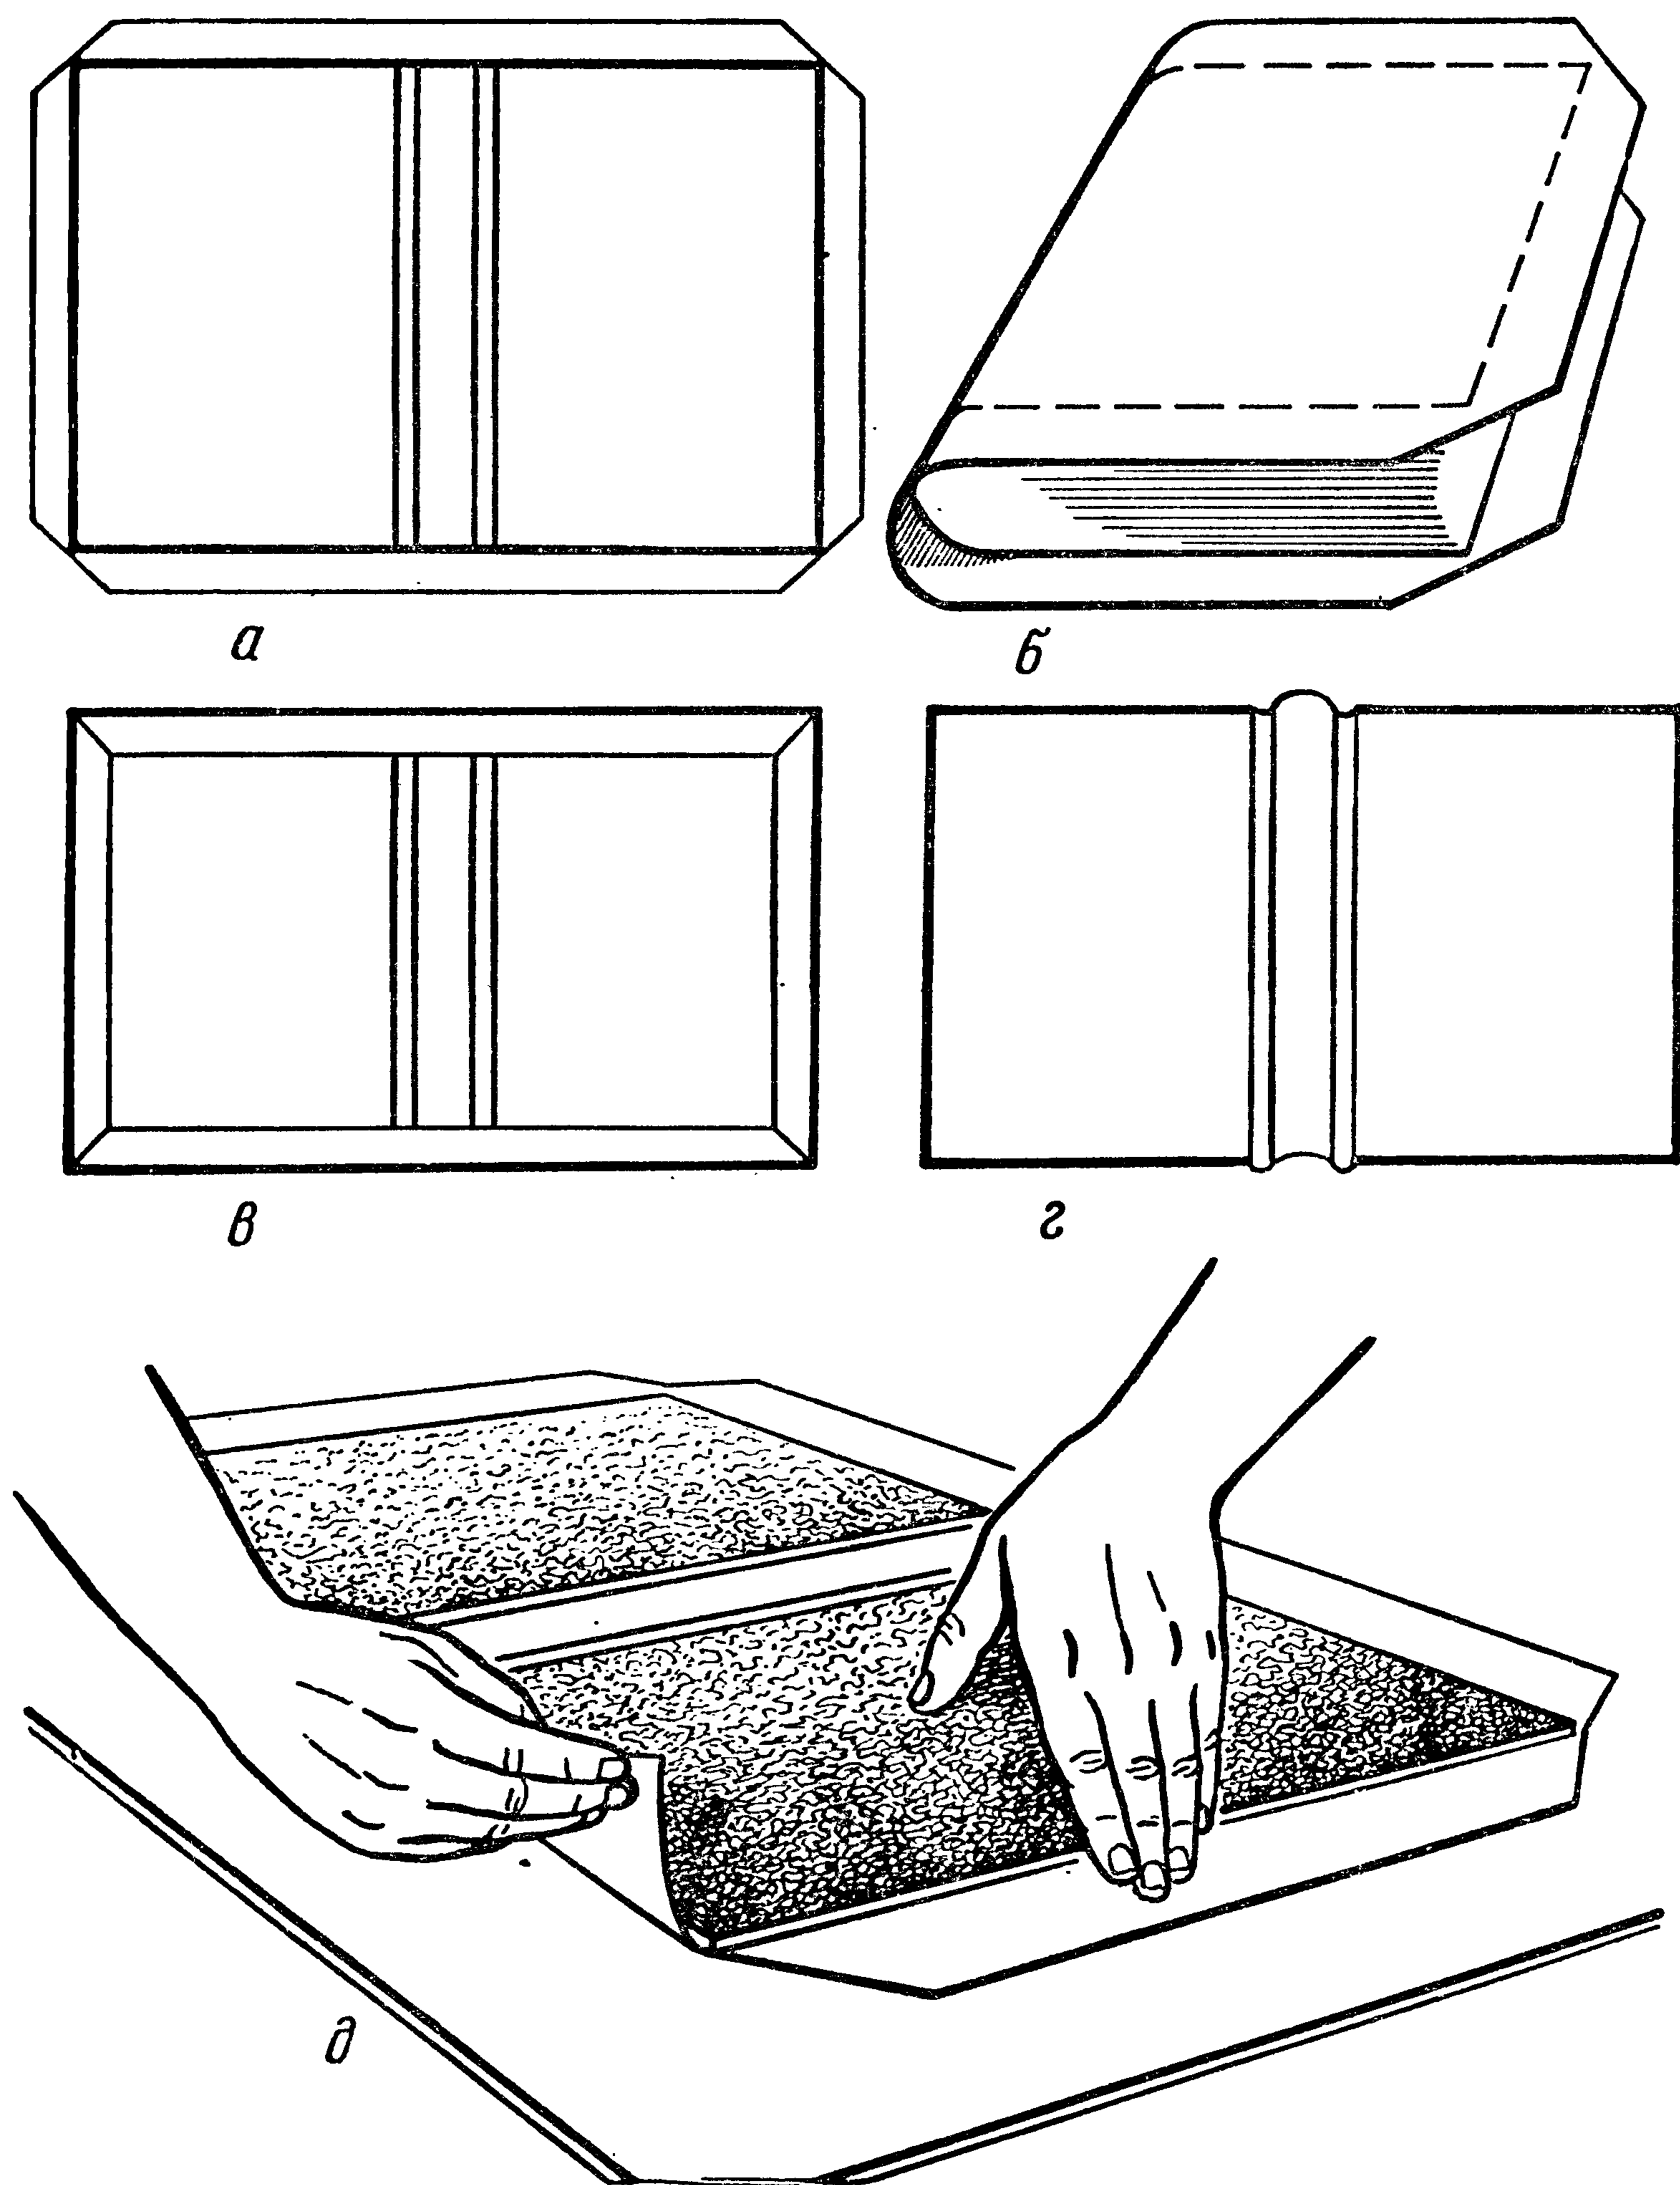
Изготовление цельнокрытой переплетной крышки: а — размещение детали на покровном материале; б — примерка крышки к книжному блоку; в — подклейка кромок покровной ткани; г — готовая крышка; д — прием загибки и подклейки кромок.
